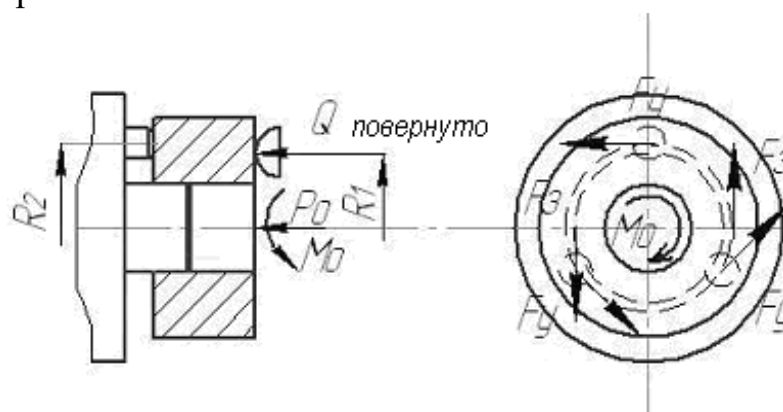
Схема встановлення заготовки на циліндричний палець та точкові опори
